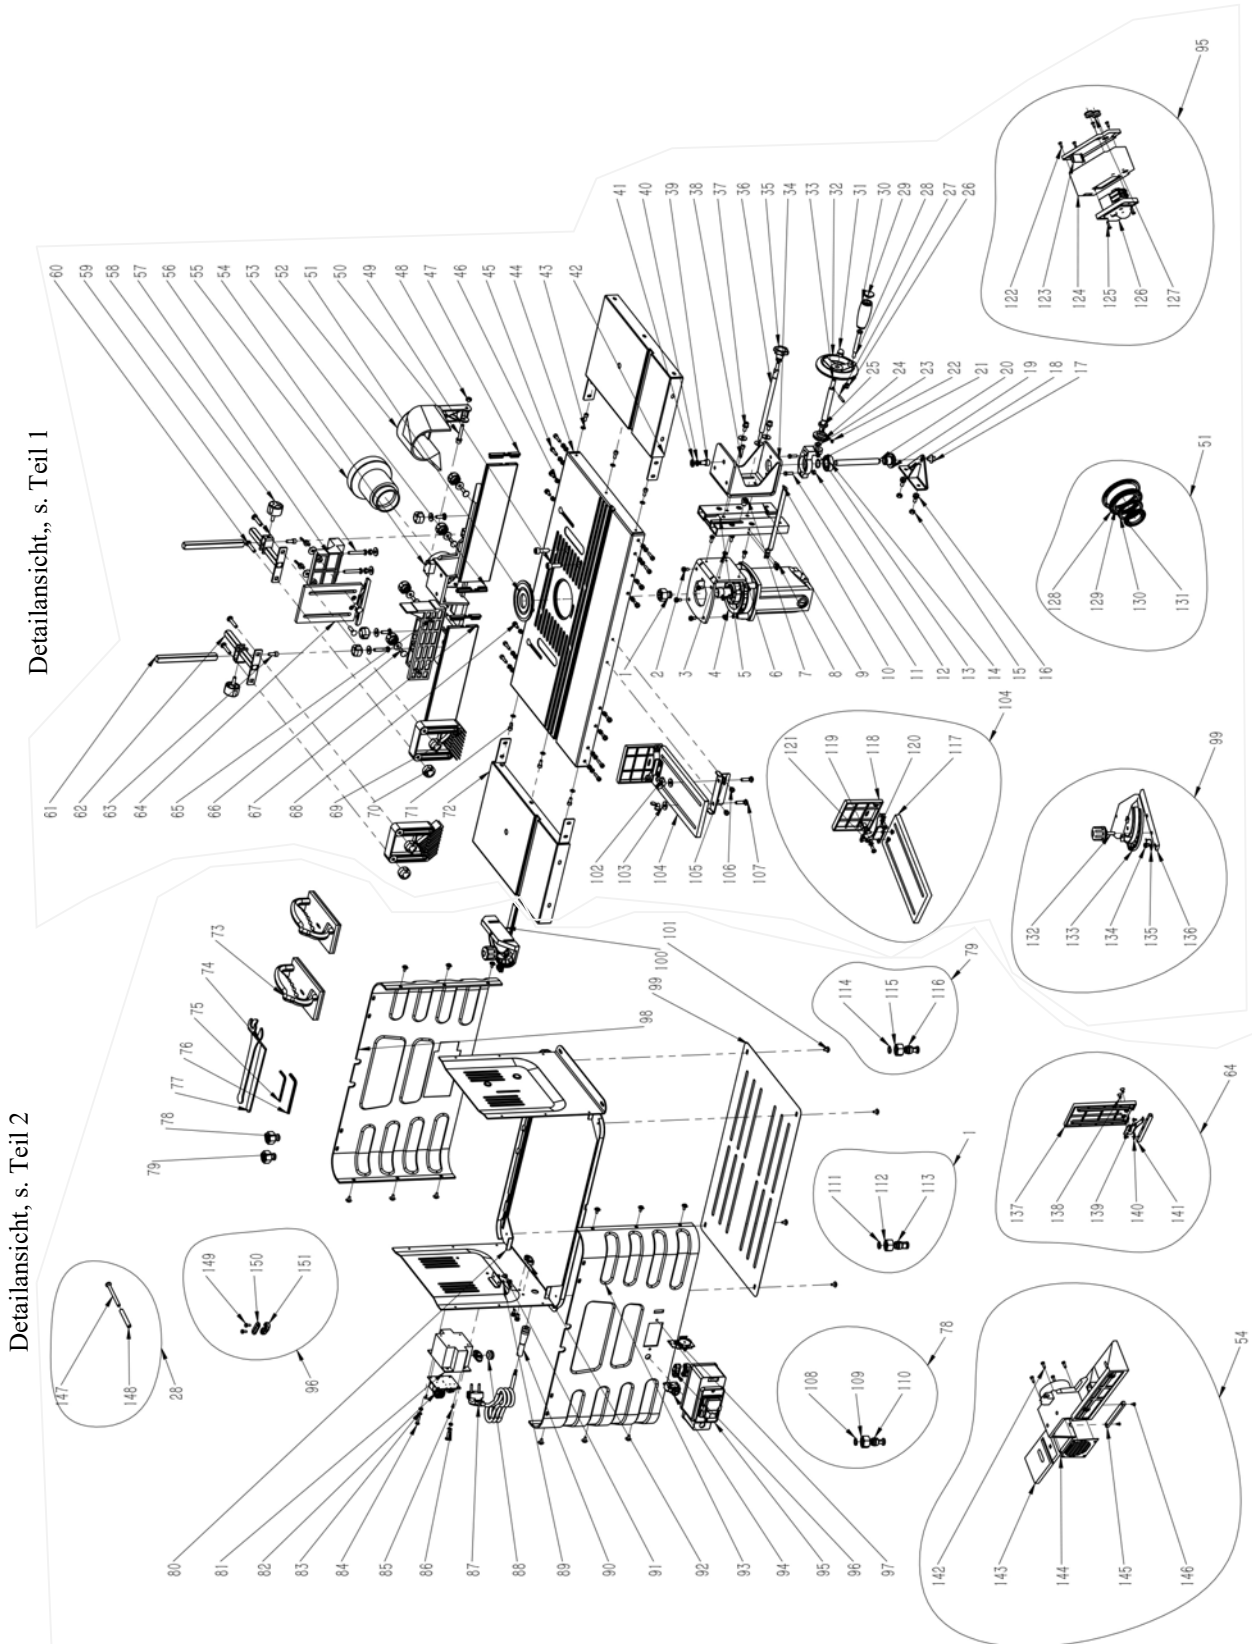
Vue éclatée TF 50 E - Vue d'ensemble
